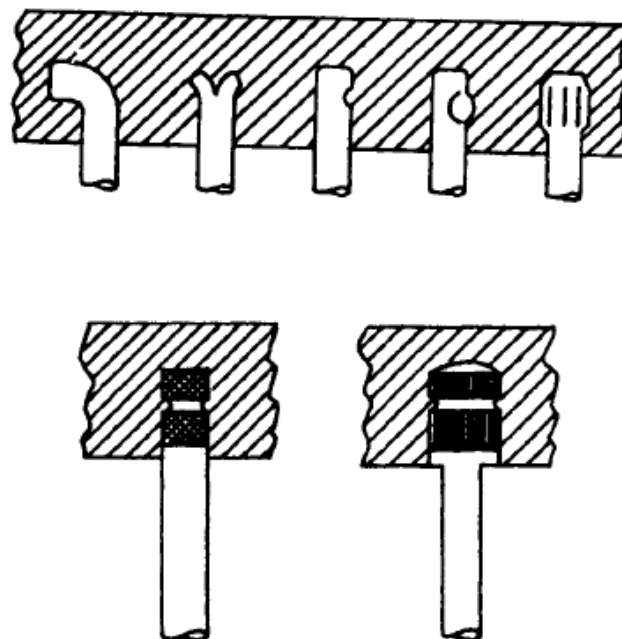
Técnicas de Design de Insertos (adaptado de [12])
